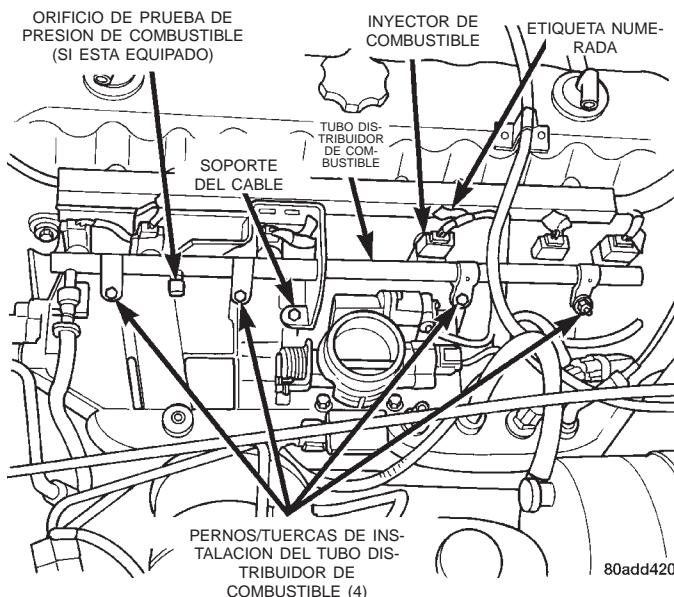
Montaje del tubo distribuidor de combustible—Motor 4.0L
